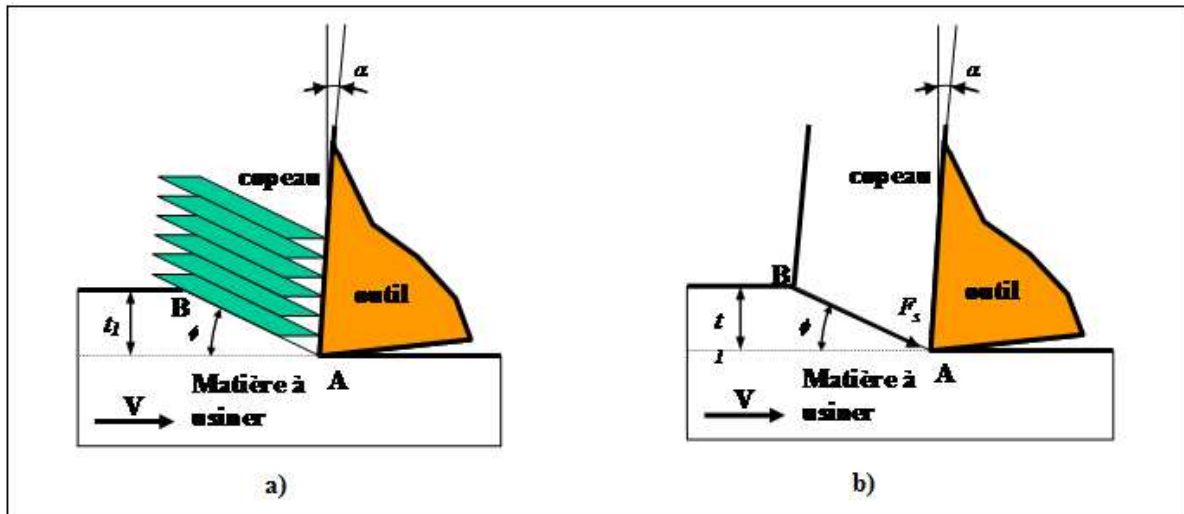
a) formation du copeau par cisaillement dans le plan AB, b) Coupe orthogonale
